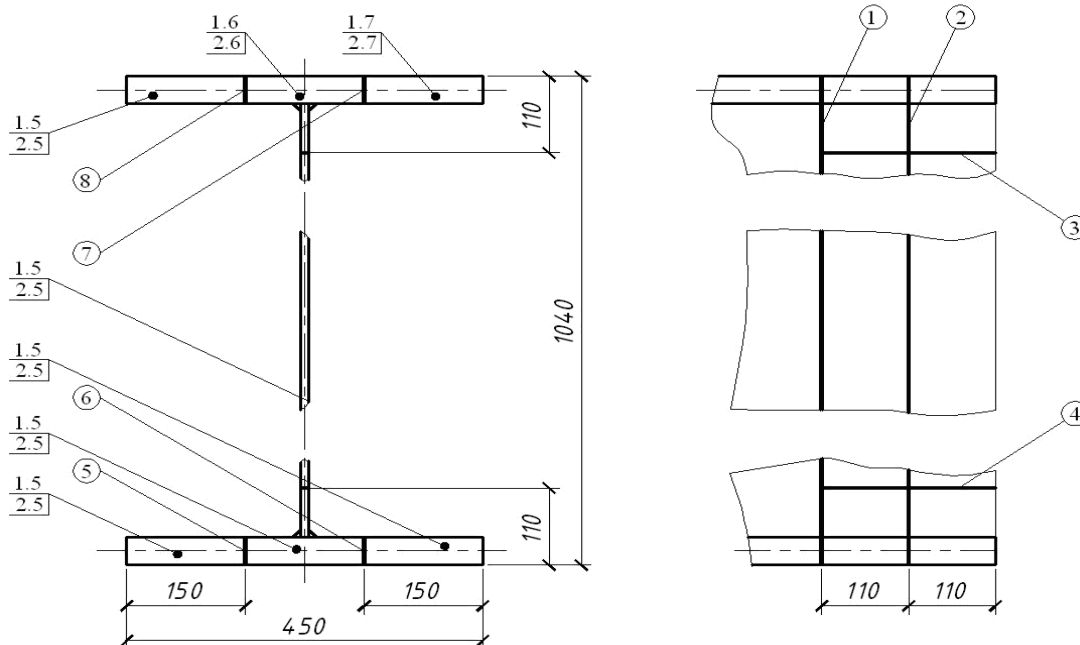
Схема відбору проб та таврування заготовок для виготовлення зразків:
